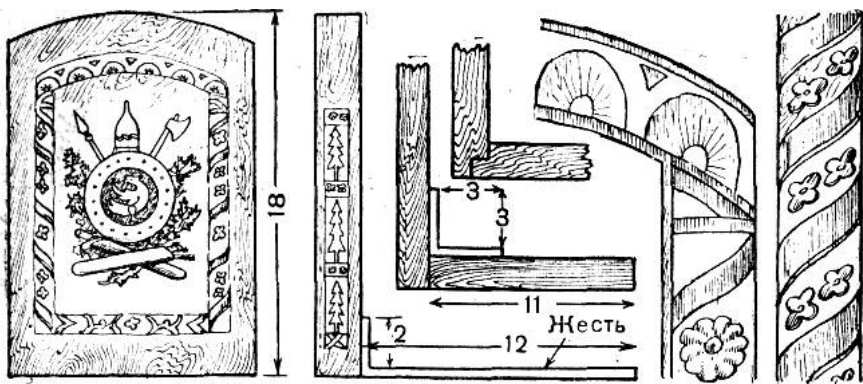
Держатель настольных книг. Поверхность дерева обрабатывается резьбой и выжиганием и лакируется.
